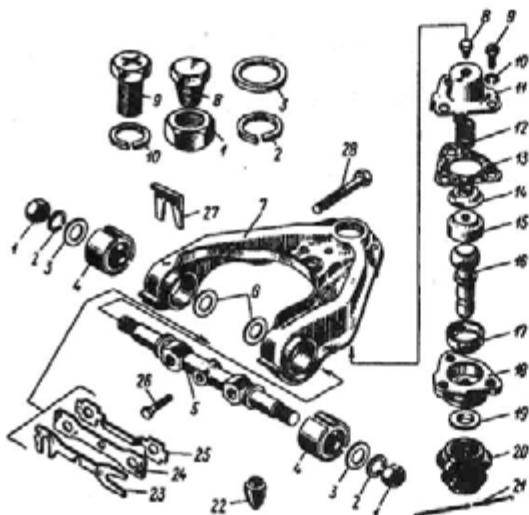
Верхний шаровой шарнир стойки и верхний рычаг с осью передней подвески
